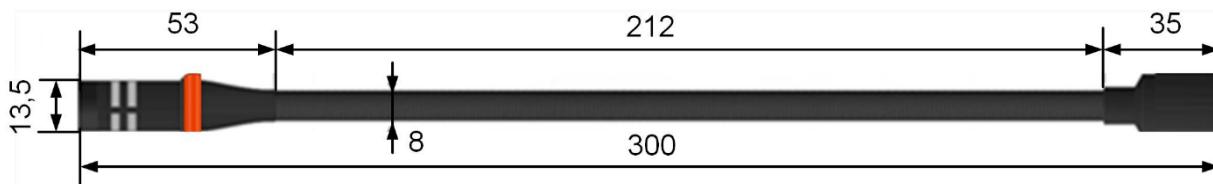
Внешний вид и габаритные размеры микрофона типа «гусиная шея»
